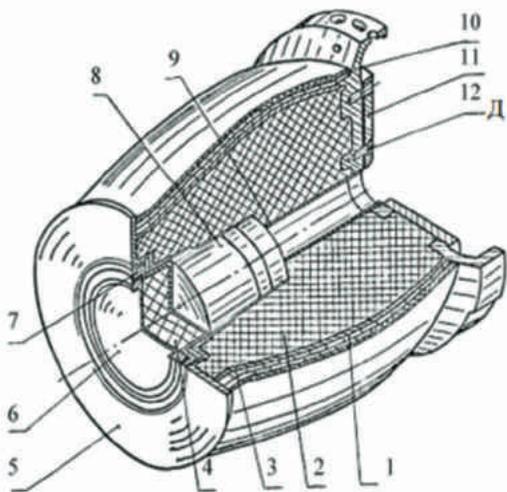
Боевая часть: 1 - поражающие элементы; 2 - заряд ВВ; 3, 9 - оболочка; 4 - шашка; 5, 10 - фланец; 6, 11 - крышка; 7 - гайка; 8 - ПНМ; 12 - винт
